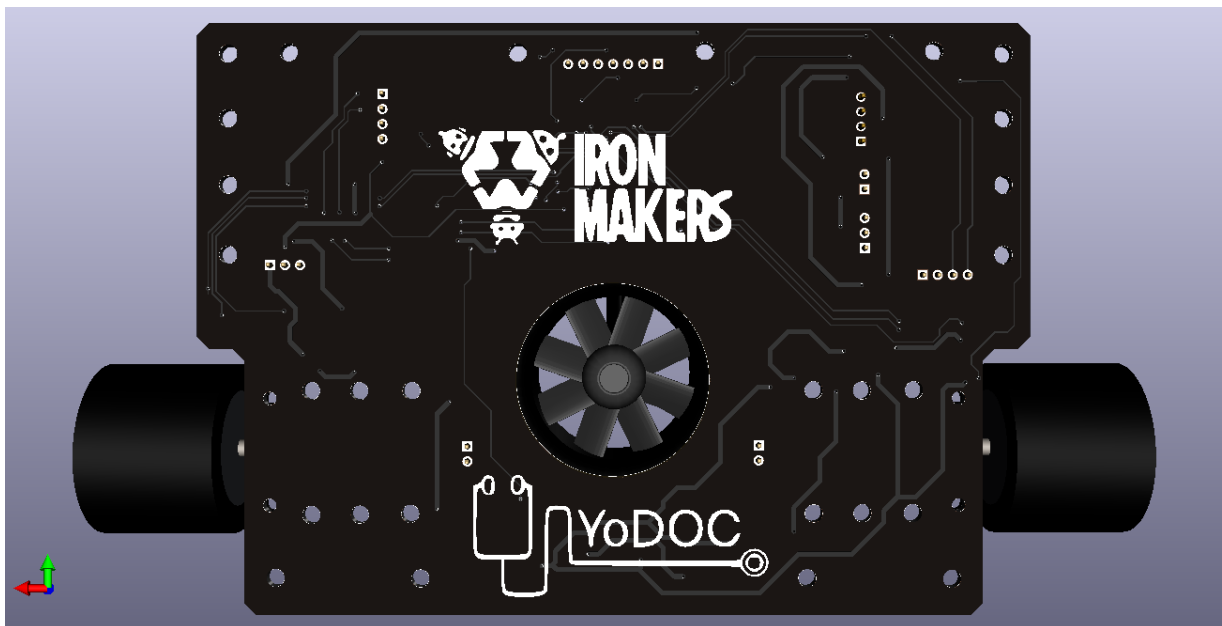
Vista Trasera en 3D de la PCB del Robot Seguidor de Línea en KiCad.
